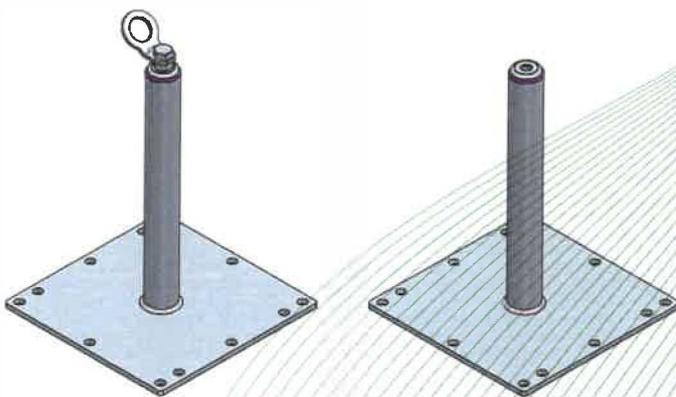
2 : Dispositif d'ancrage, type : STA-10
